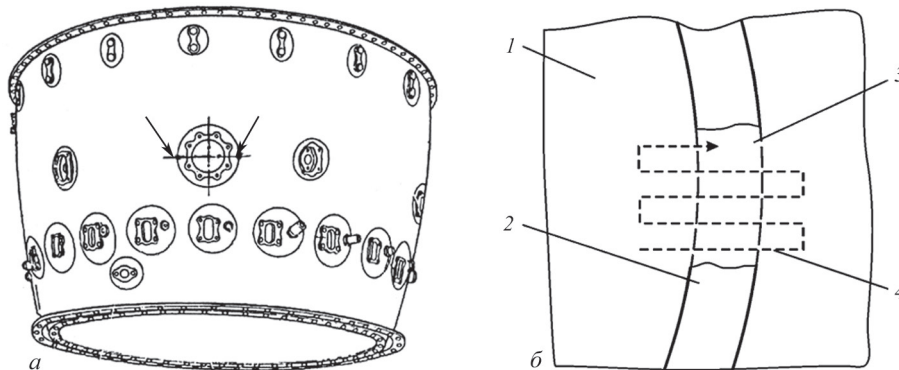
Корпус камери згоряння (а) і схема контролю зварних швів (б): 1 – корпус камери; 2 – зварний шов; 3 – зона зачистки і контролю; 4 – схема сканування
